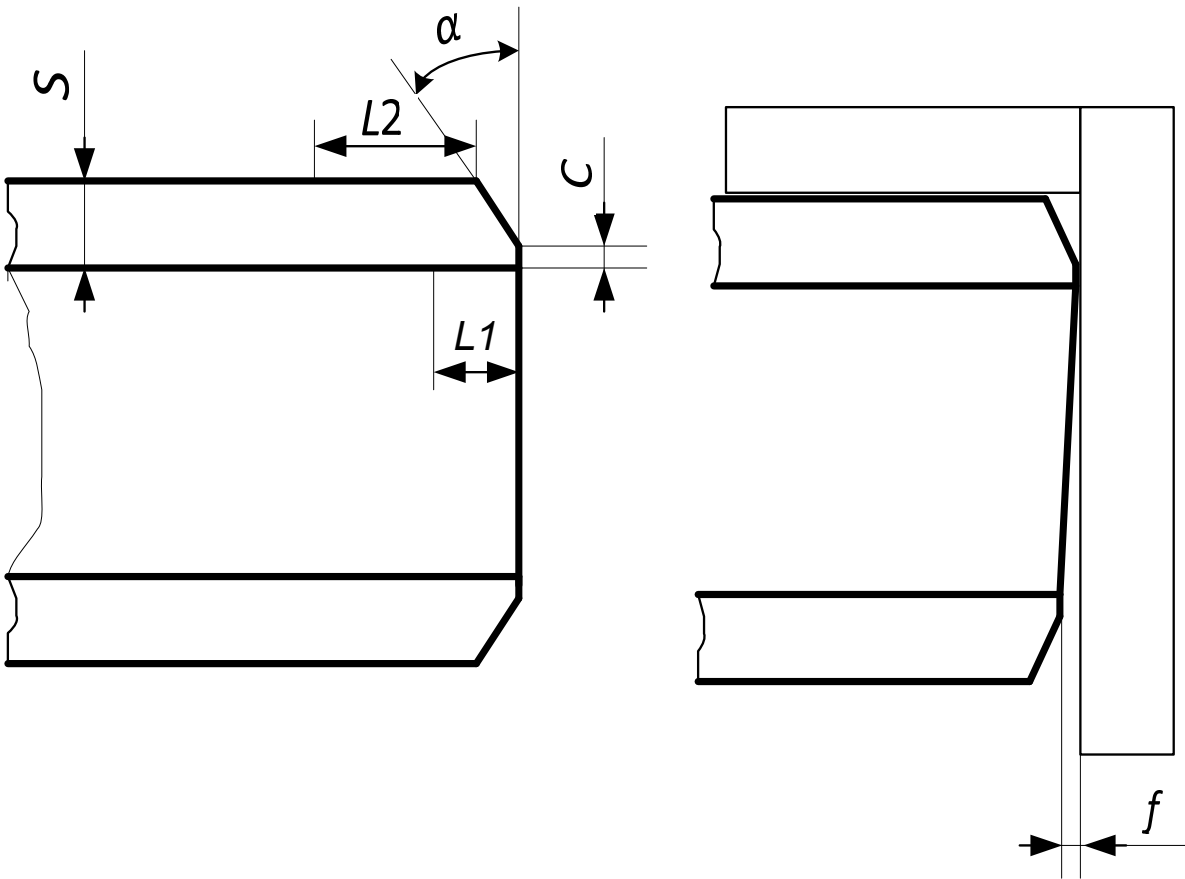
Эскиз контролируемого изделия при подготовке деталей под сварку (труба)
